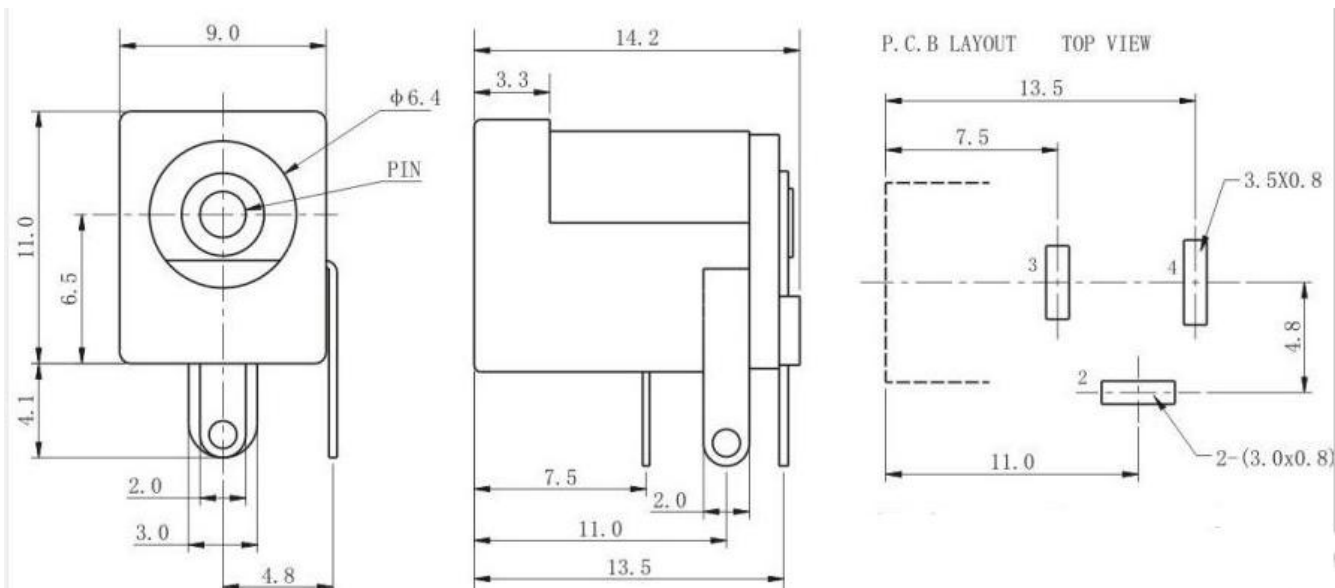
Габаритні розміри роз'єму живлення DC power jack
